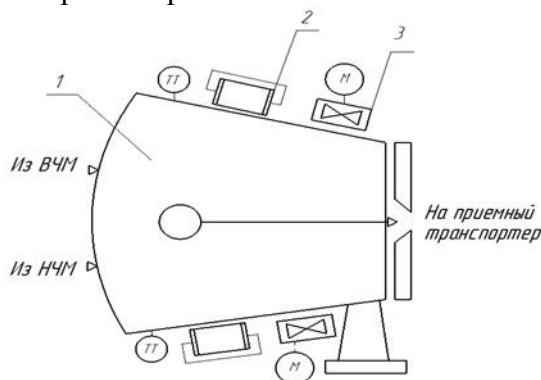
Схема головки агрегата (1 – общая головка агрегата, 2 – ТЭН, 3 – вентилятор)
